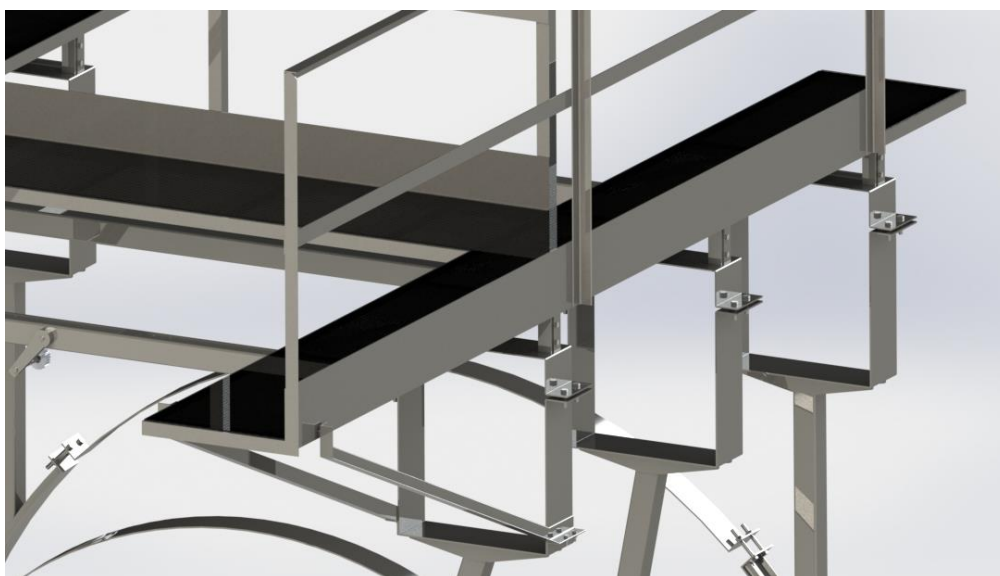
zunchos lado pontón (detalle anclaje de plataforma)
